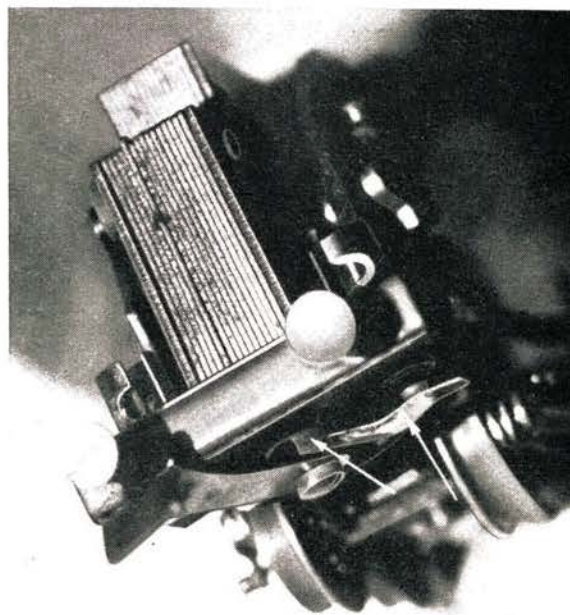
Eingebauter Lampenhalter mit bereits eingefeilten Lichtaustritten.
